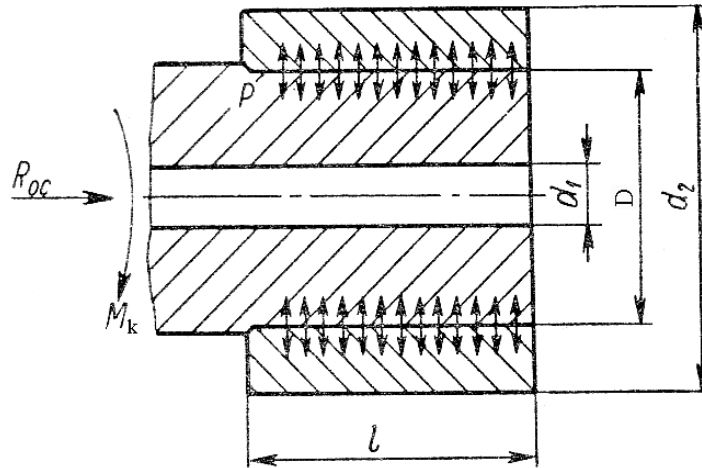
Схема з'єднання двох деталей за посадкою з натягом
